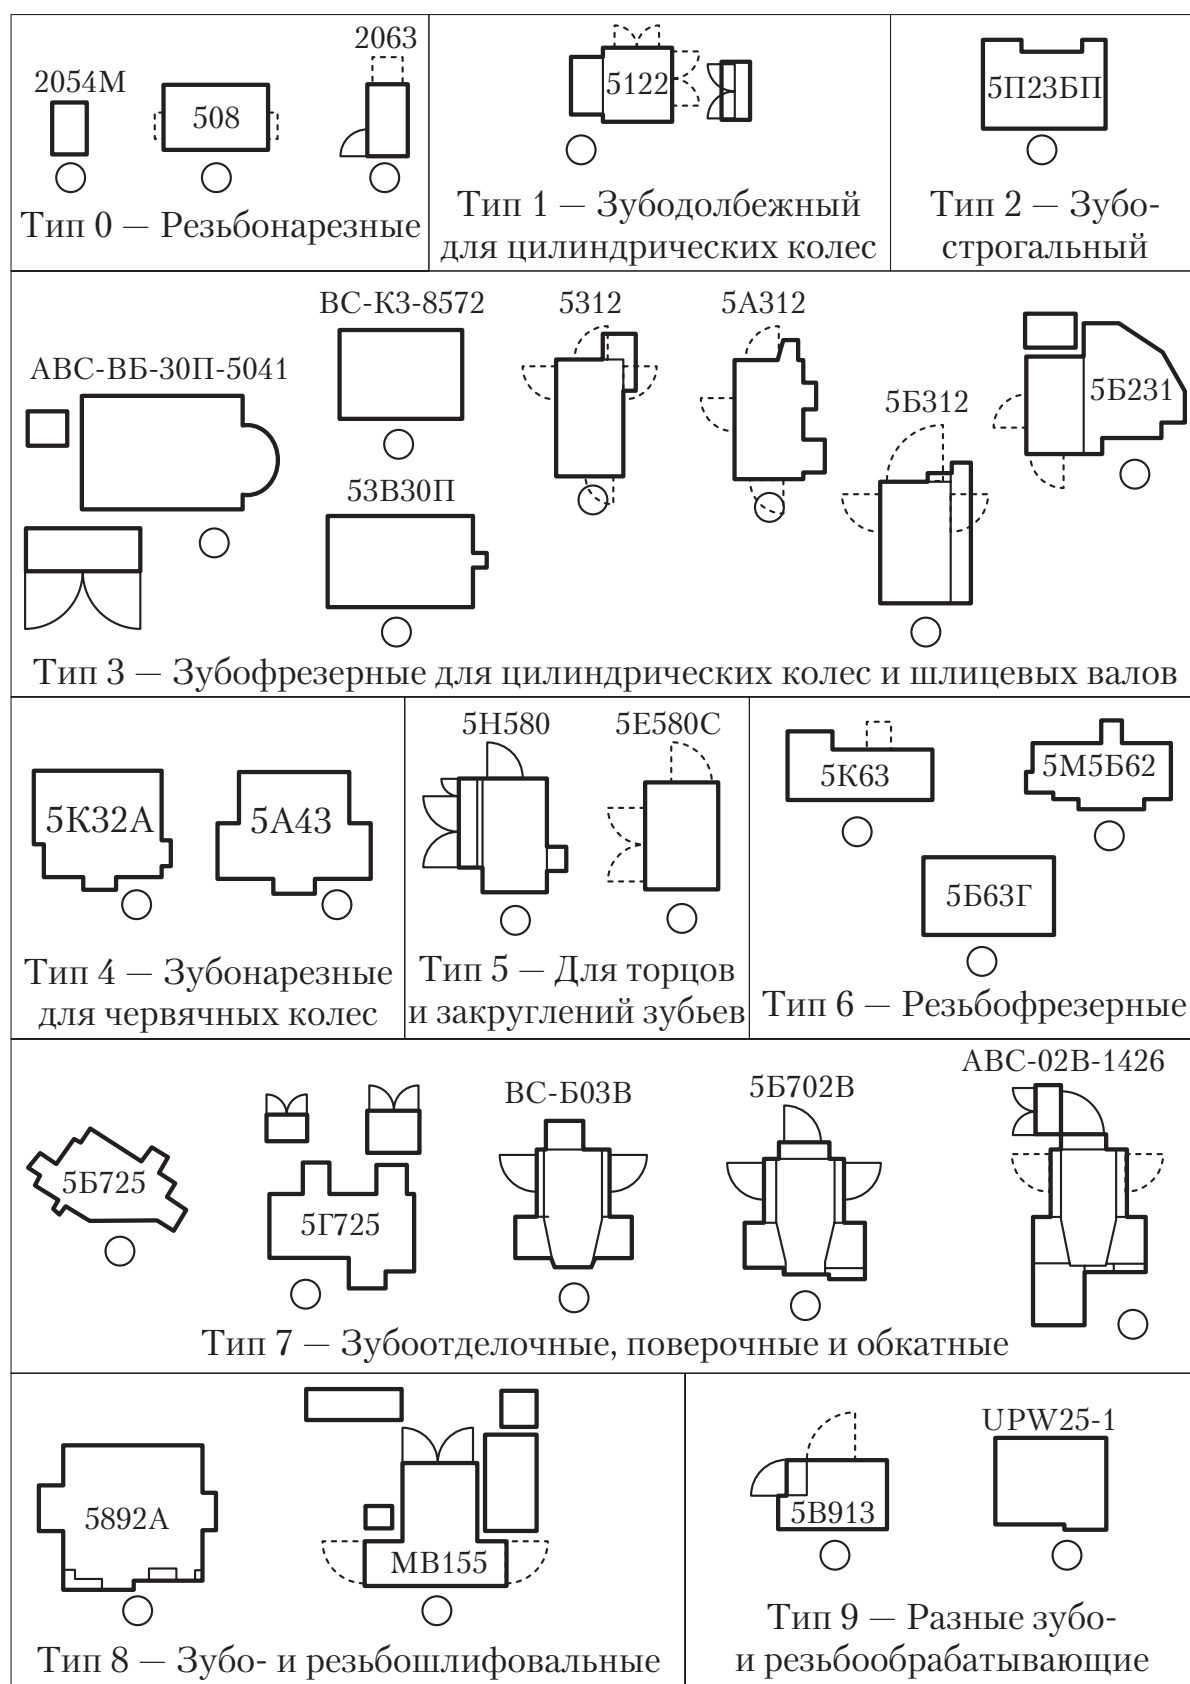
Габаритные планы некоторых станков группы 5 — зубо- и резьбообрабатывающие типов 0–9
